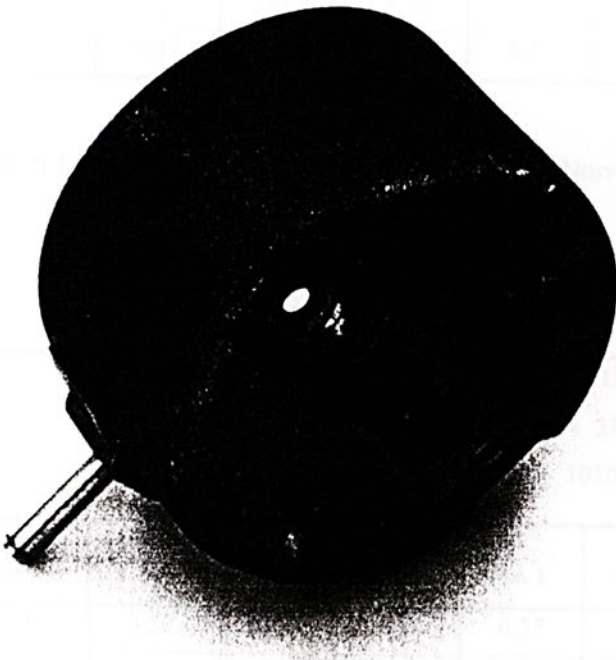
TAMPA DIANTEIRA NORMAL DO CONJUNTO ROTOR - ESTATOR
